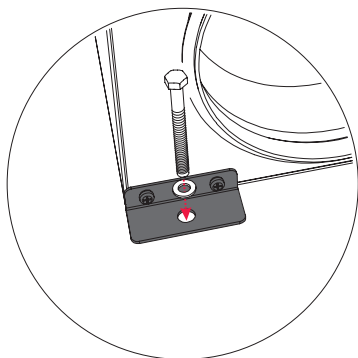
Installatie aan de muur, vloer of plafond
